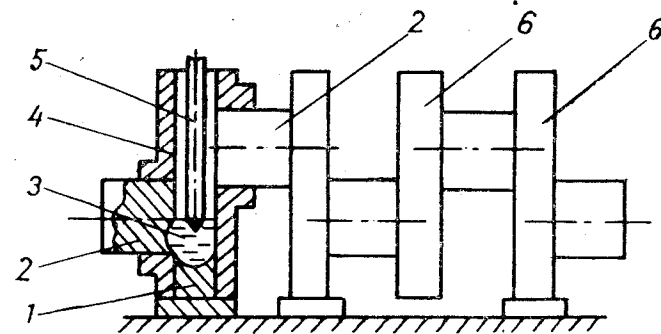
Схема виливання заготовки колінчастого вала:
